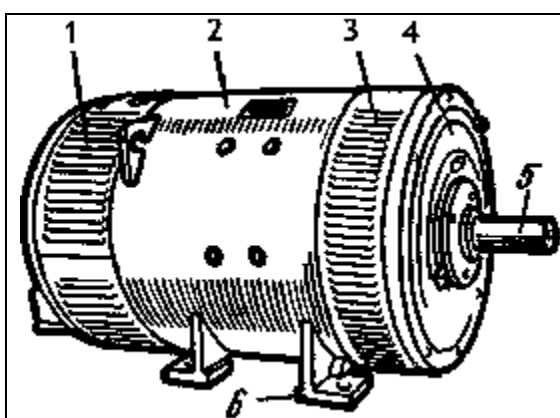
Двигатель постоянного тока защищенного исполнения (степень защиты IP22): 1, 3 — вентиляционные окна для входа и выхода охлаждающего воздуха; 2 — станина; 4 — подшипниковый щит; 5 — вал; 6 — лапы
